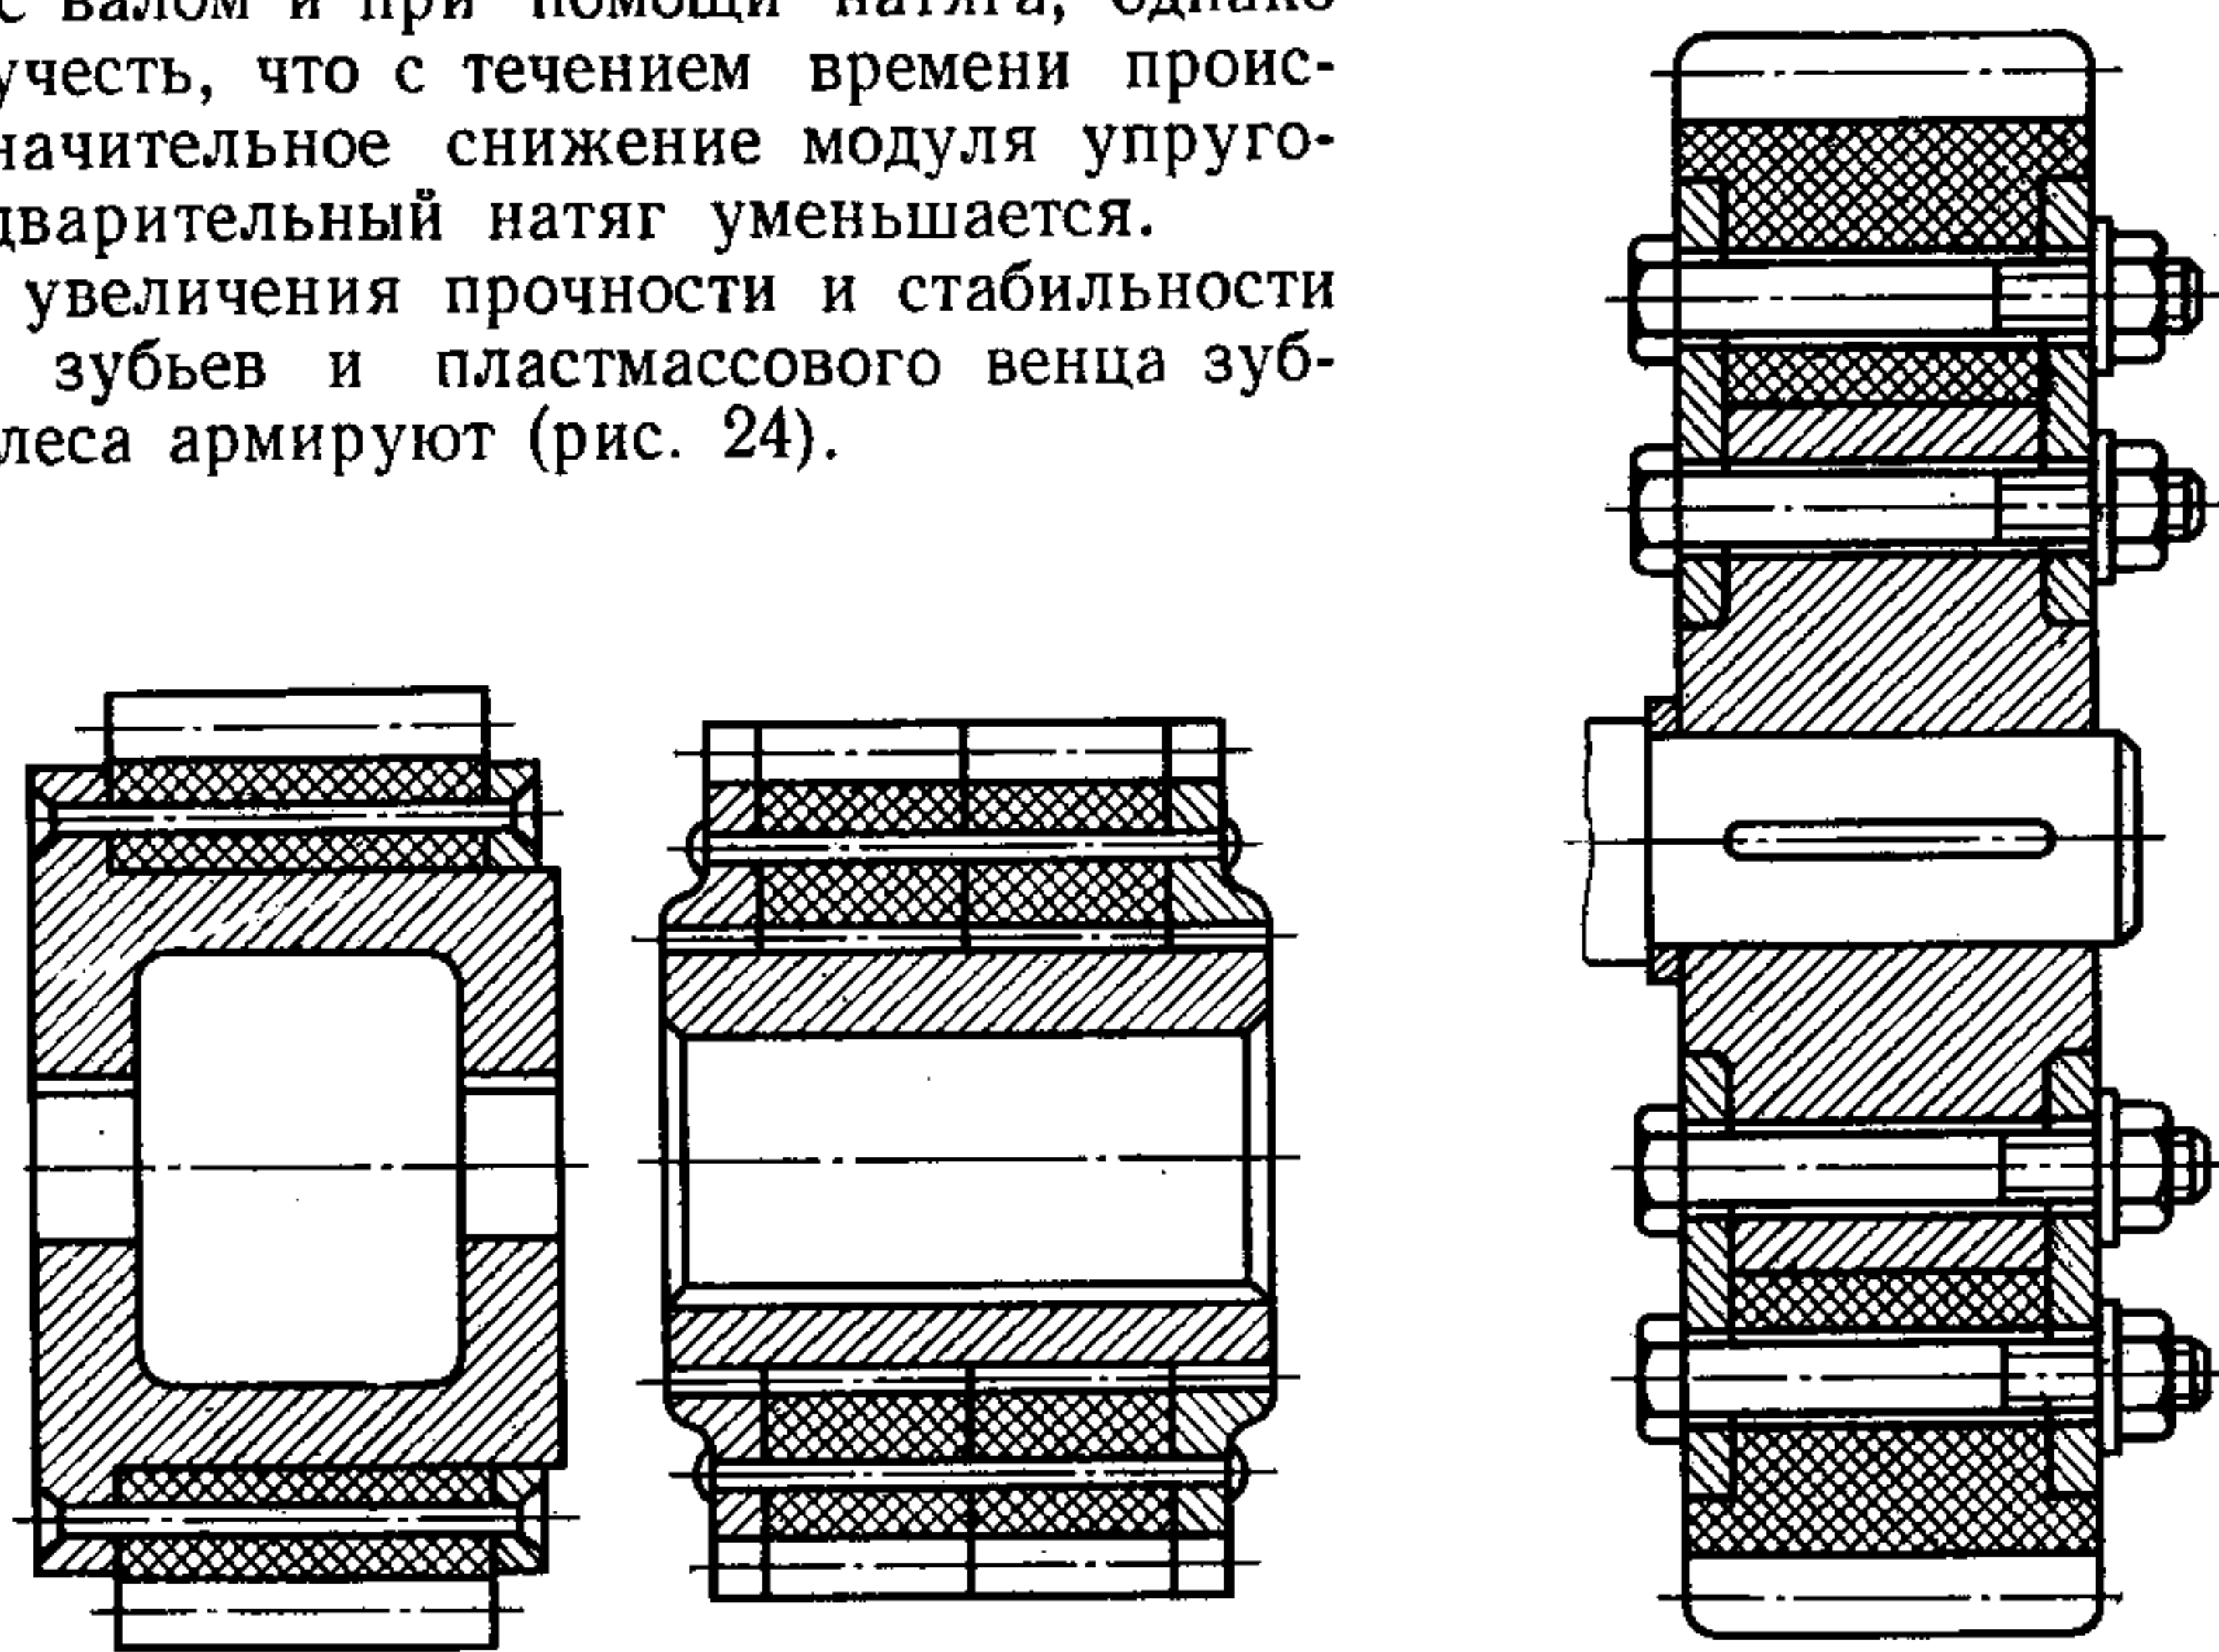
Примеры армирования зубчатых колес из пластмасс
